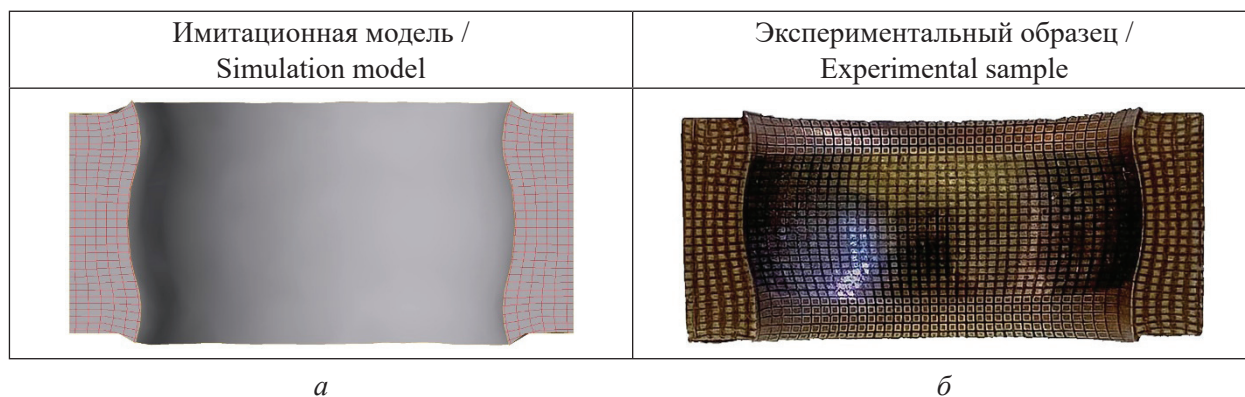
Сечение наружного кольца сферического подшипника с координатной сеткой после штамповки пуансонами:
